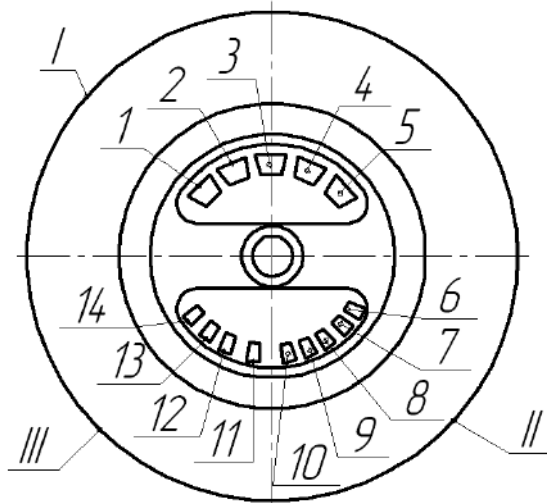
Знаки маркировки и клейма на правом торце оси колесной пары с подшипниками качения с торцовым креплением гайкой
